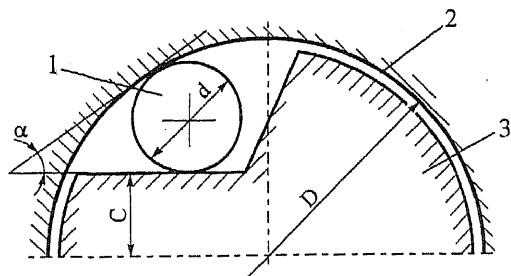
Расчетная схема муфты свободного хода с плоской рабочей поверхностью звездочки: 1 — ролик; 2 — обойма; 3 — звездочка; α — угол заклинивания; d, D — диаметр ролика и обоймы соответственно
